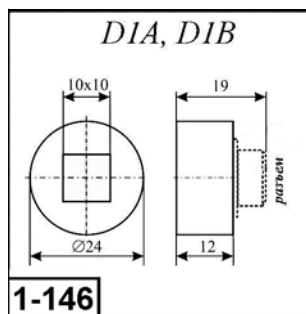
Внешний вид и габаритные размеры детекторов Д1А - Д30В
